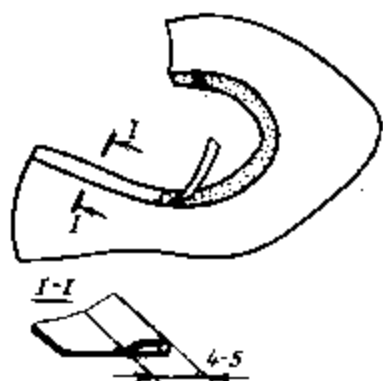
Загибка краев деталей верха с вклеиванием тесьмы
